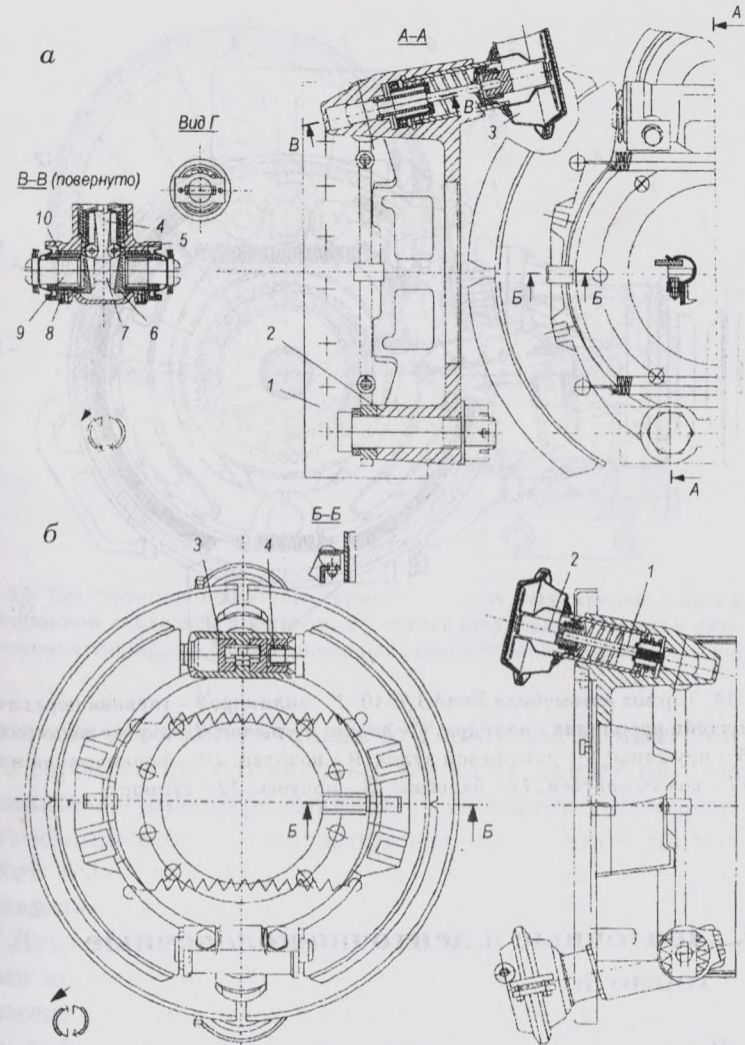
Схема барабанных тормозов автомобиля «Колхида»: *а* – с односторонним расположением опорных поверхностей (задний тормоз автомобиля КАЗ-4540): 1 – колодка; 2 – суппорт (тормозной щит); 3 – тормозная камера; 4 – клин; 5 – ролик; 6 – плунжер; 7 – упор; 8 – собачка; 9 – регулировочный винт; 10 – регулировочная втулка; *б* – с разнесенными опорными поверхностями (передний тормоз автомобиля КАЗ-4540): 1 – шток; 2 – толкатель; 3 – разжимное устройство; 4 – толкатель разжимного устройства
